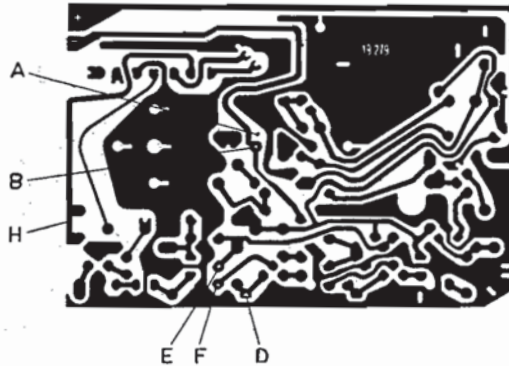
Cablaggio stampato di piccolo apparecchio a transistor.
